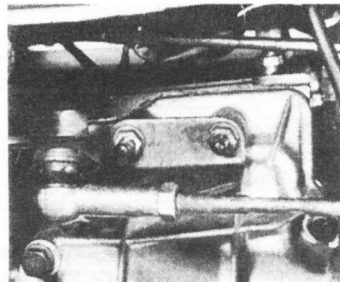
Крепежные гайки опорной скобы передаточного рычага
